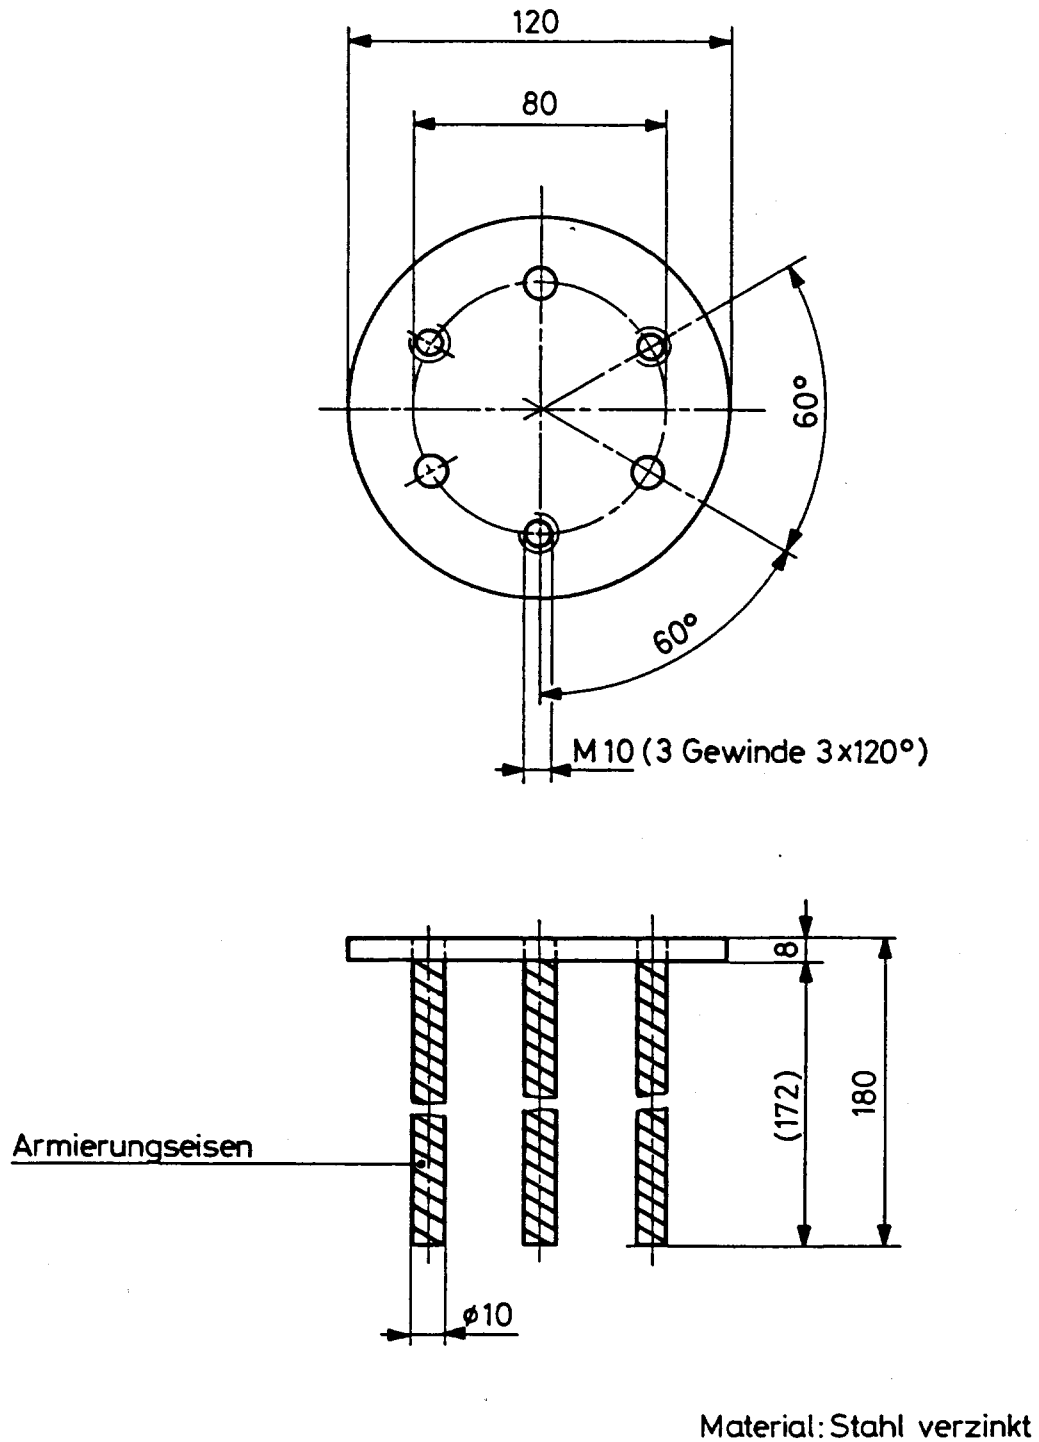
Flansch für die Montage der Stahlpfeiler
